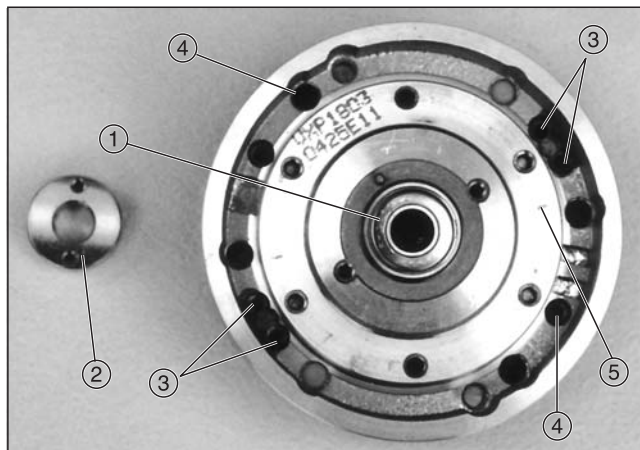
Верхний цилиндр VXP1803 (вид сверху)
